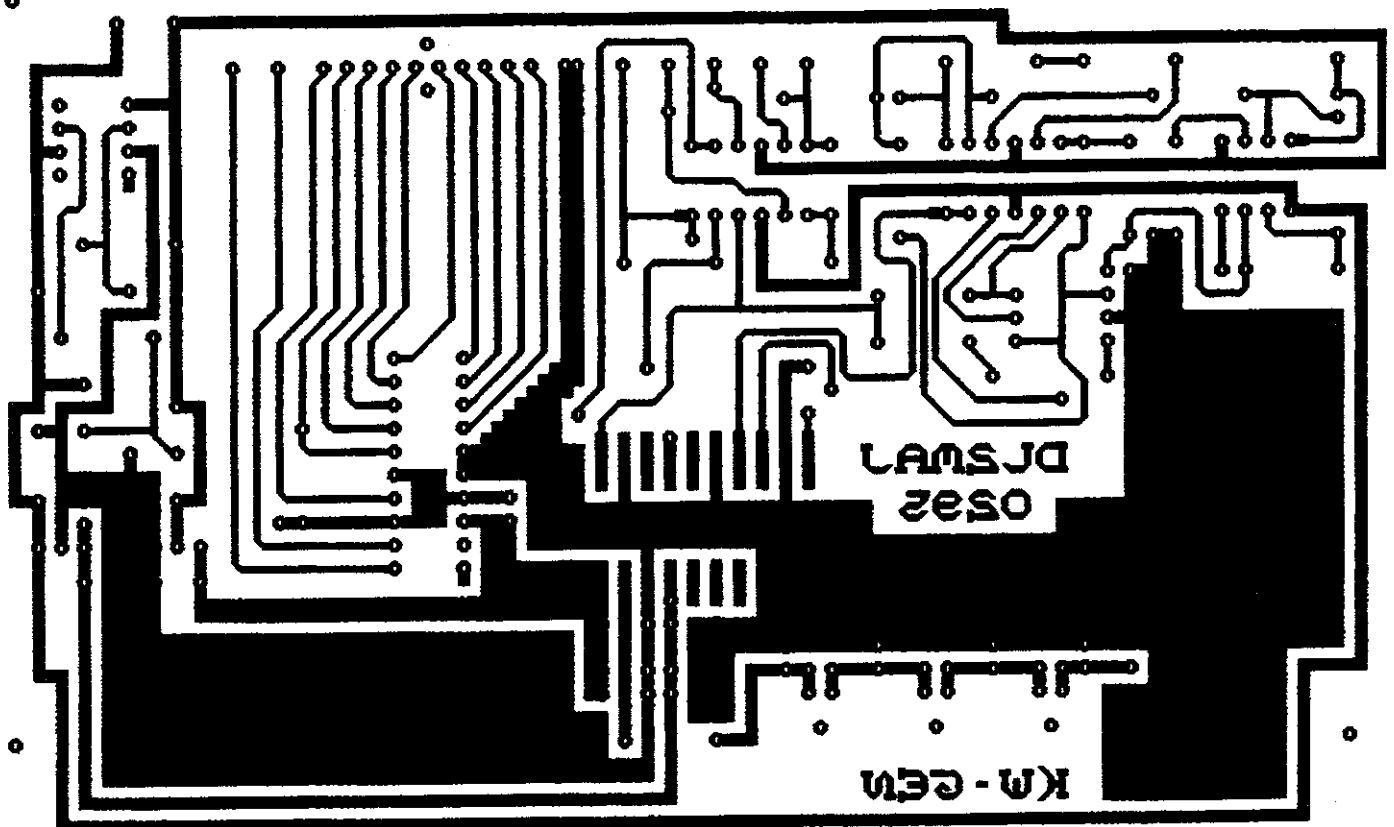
Printlayout. MAX038 monteres oven på printet.
